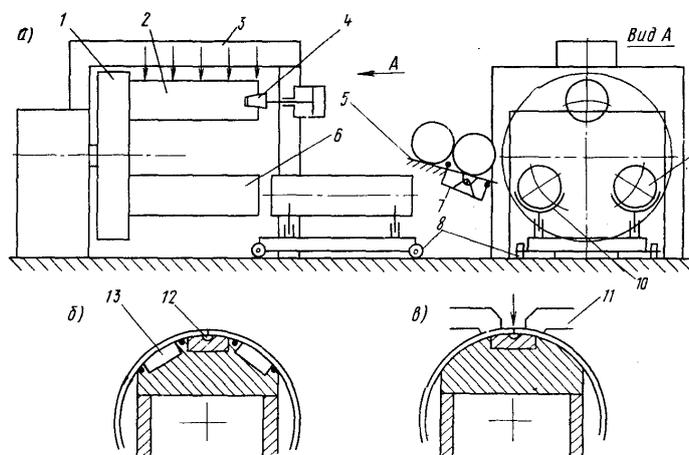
Полуавтоматическая установка для сборки и сварки продольного стыка обечайки:
